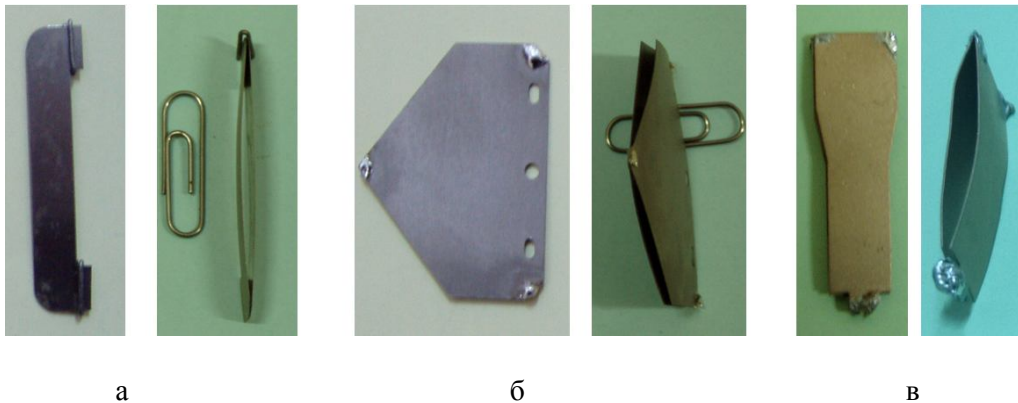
Внешний вид спаренных деталей до и после абразивной обработки затопленными струями: а – материал ВТ-1; б – сталь 65Г; в – бериллиевая бронза БрБ2
